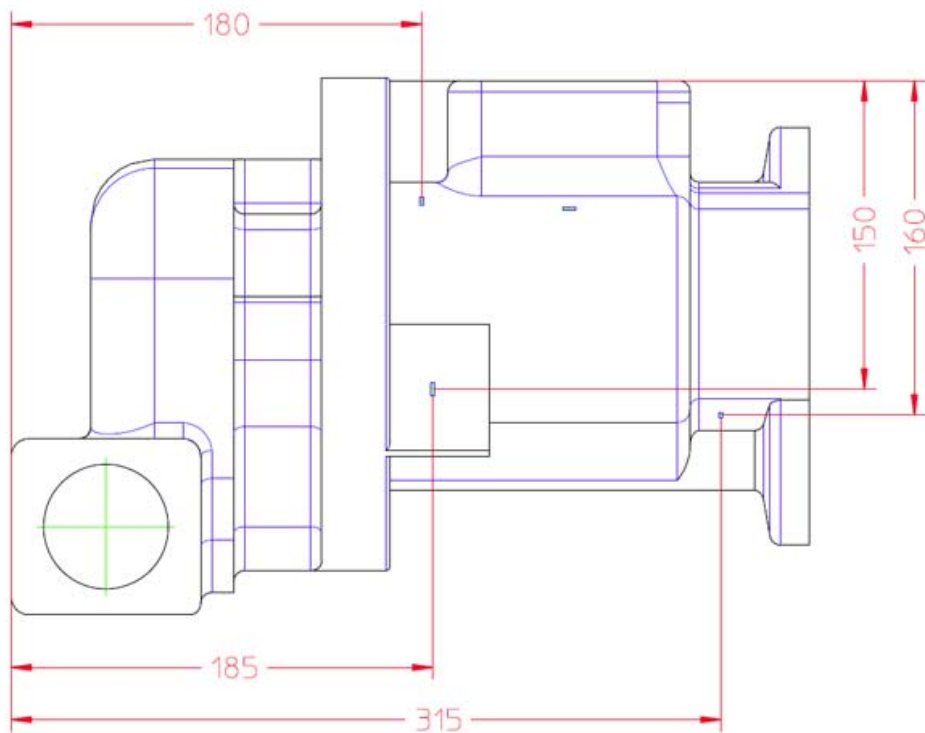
Bemaßung der Messstellen Seitenansicht Nebenläufer
